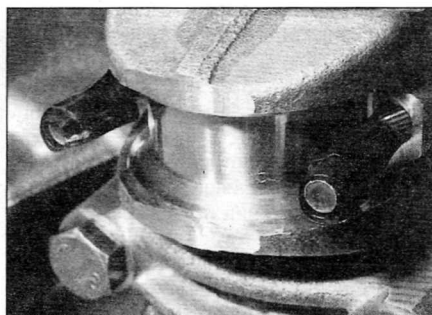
Для защиты шеек коленчатого вала заклейте липкой лентой резьбовые концы шпилек шатуна
